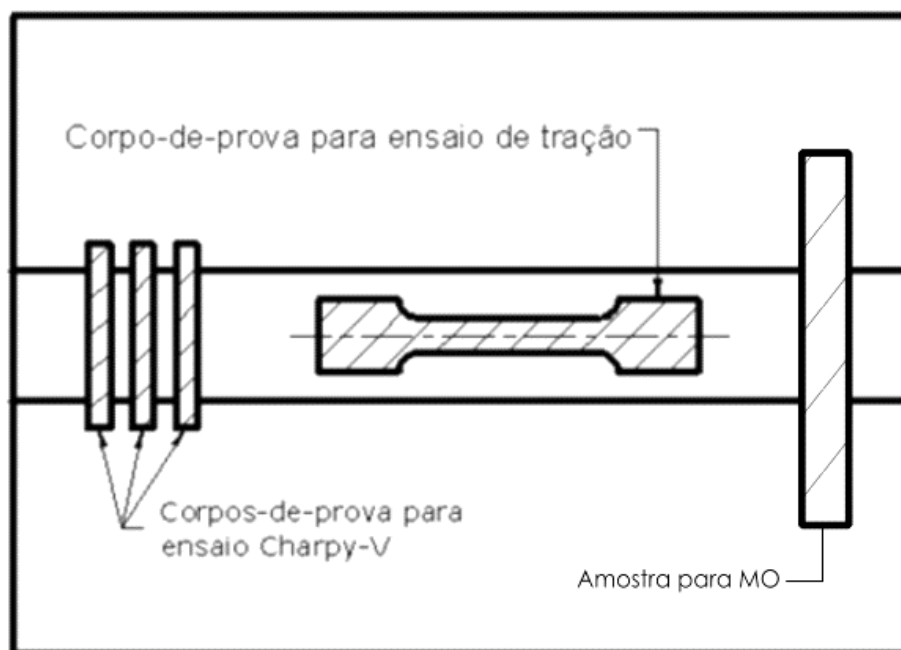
Detalhe da posição de retirada dos corpos-de-prova para ensaio de tração e impacto Charpy-V, em relação à junta soldada.
